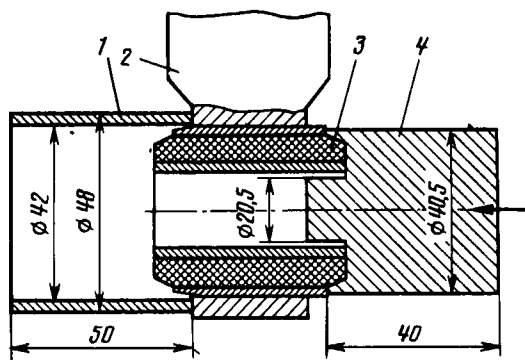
Выпрессовка сайлент-блока из амортизатора задней подвески:
